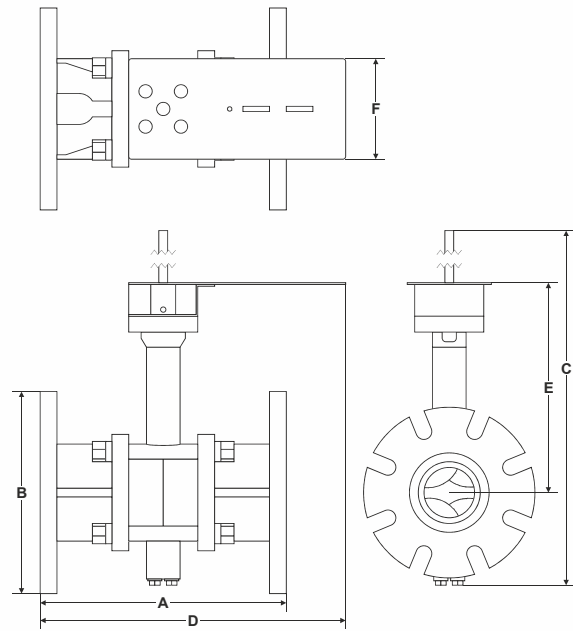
2-Wege-Ventile DN 100 ... 150 Abmessungen
